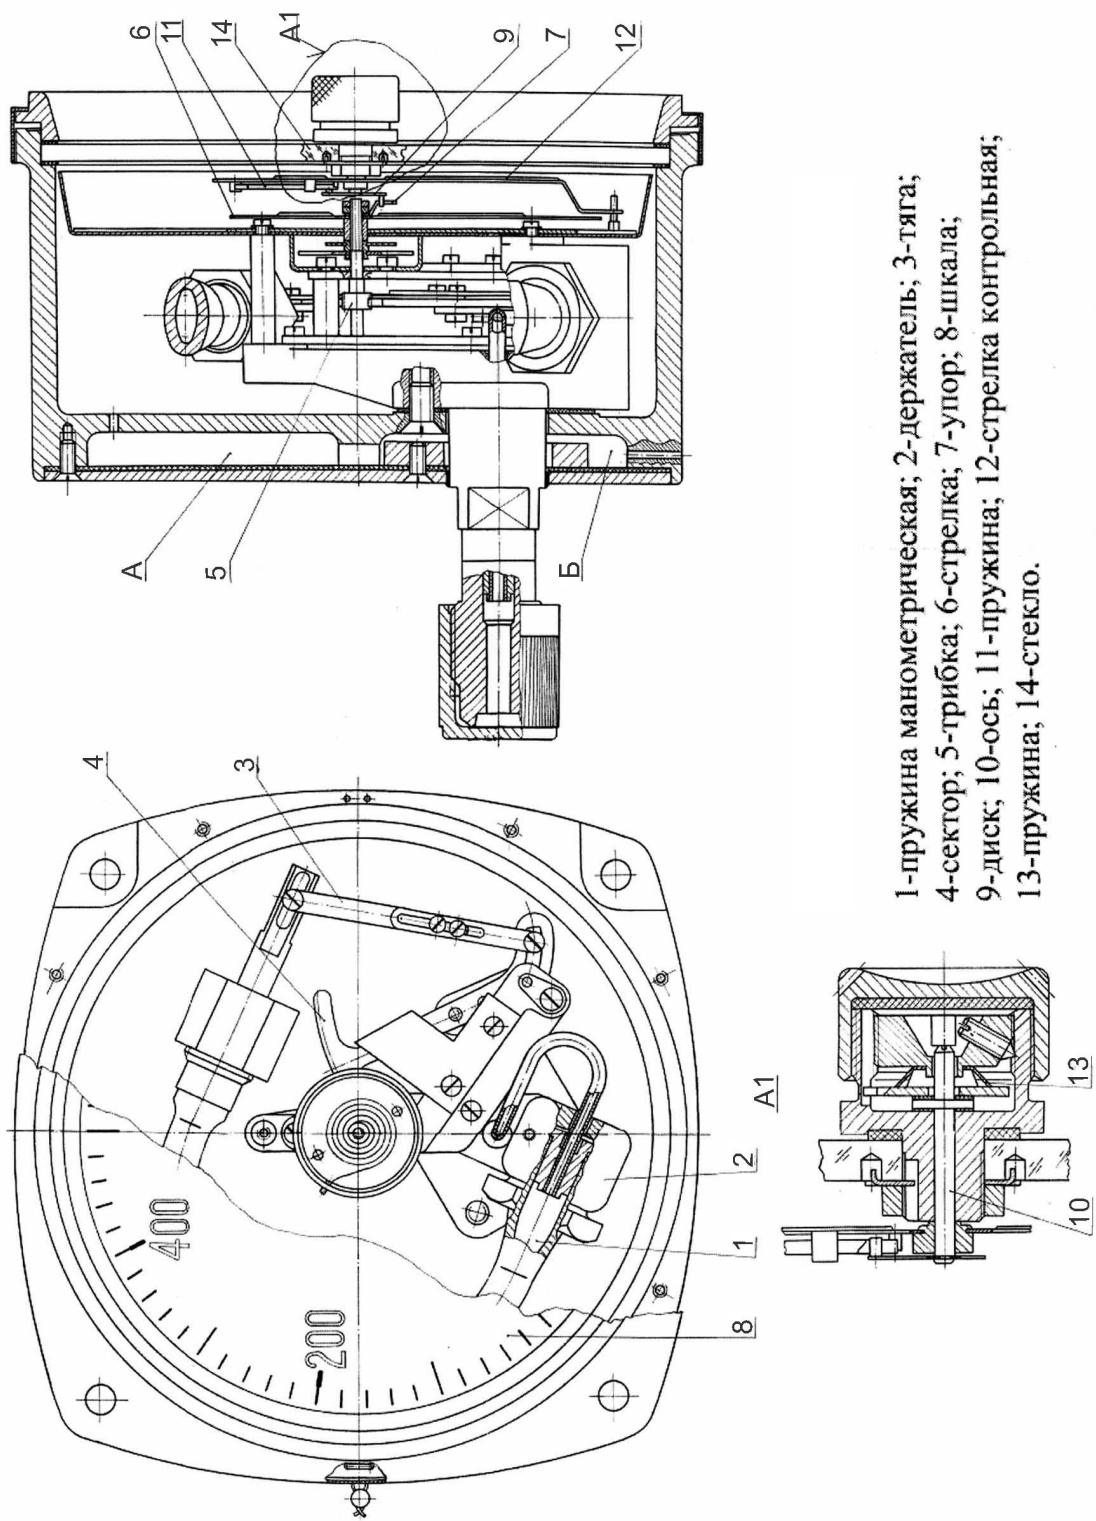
Габаритно-монтажный чертёж манометра МКР-160С.
